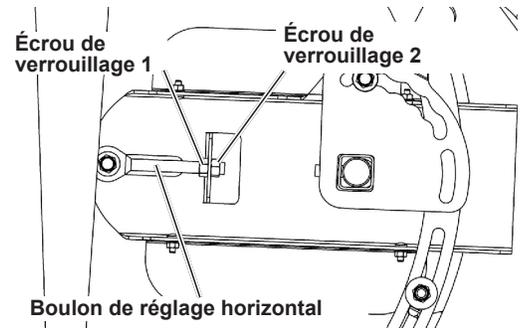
Réglage avant/arrière du tambour de la vis d'alimentation
